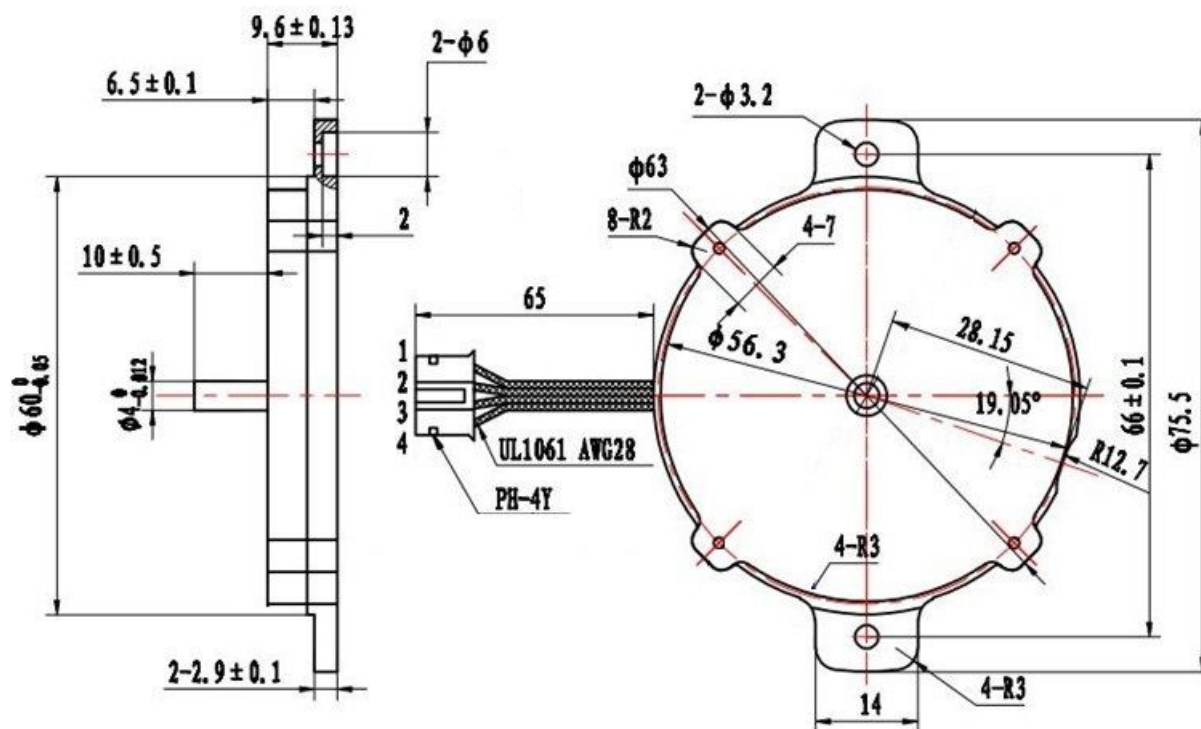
Габаритные размеры шаговых двигателей серии 57BYGH10
